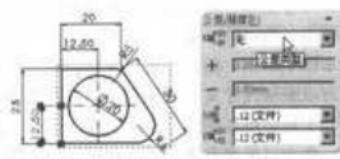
选择尺寸并设置尺寸公差/精度
